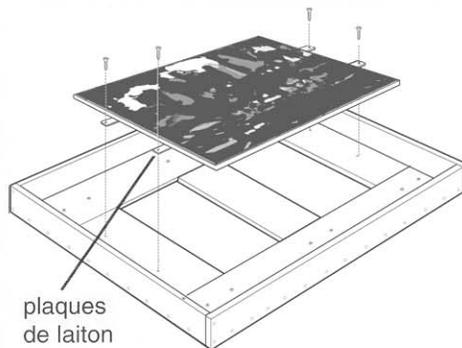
Installation d'un tableau dans un cadre de transport ou d'entreposage.
